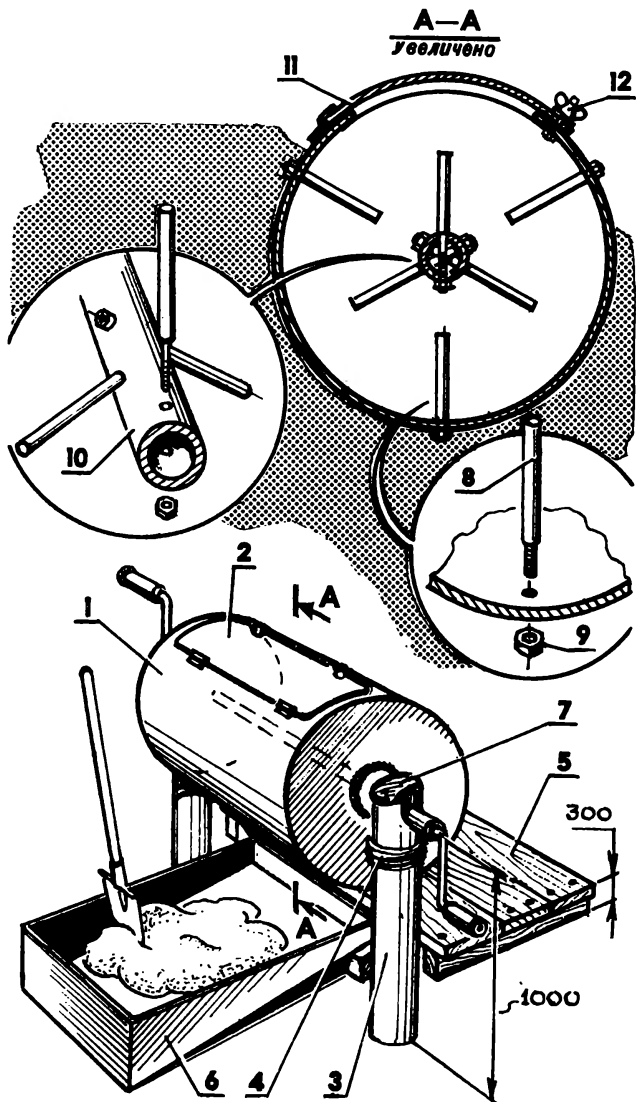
Растворомешалка, изготовленная из бочки: 1 — бочка, 2 — крышка, 3 — стойки, 4 — бандаж, 5 — помост, 6 — ящик для раствора, 7 — защитная резина, 8 — штыри из прутка с резьбой, 9 — гайка, 10 — ось, 11 — уплотнительная прокладка, 12 — барашек.
